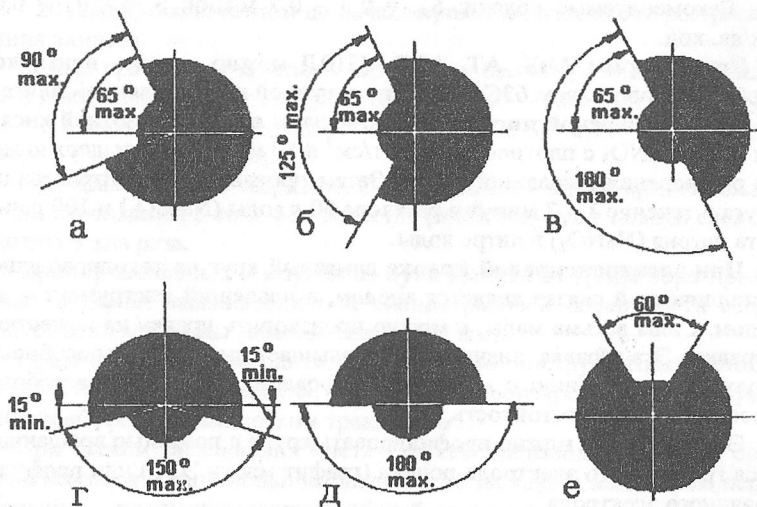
Углы раскрытия защитных кожухов шлифовальных кругов: а – на обдирочных и заточных станках; б – то же, но когда при работе деталь располагается ниже оси круга; в – на кругло- и бесцентровошлифовальных станках; г – на плоскошлифовальных станках, работающих периферией круга; д – на переносных станках с гибким валом и обдирочных с качающейся рамой; е – для станков, работающих наиболее высокой точкой круга.
